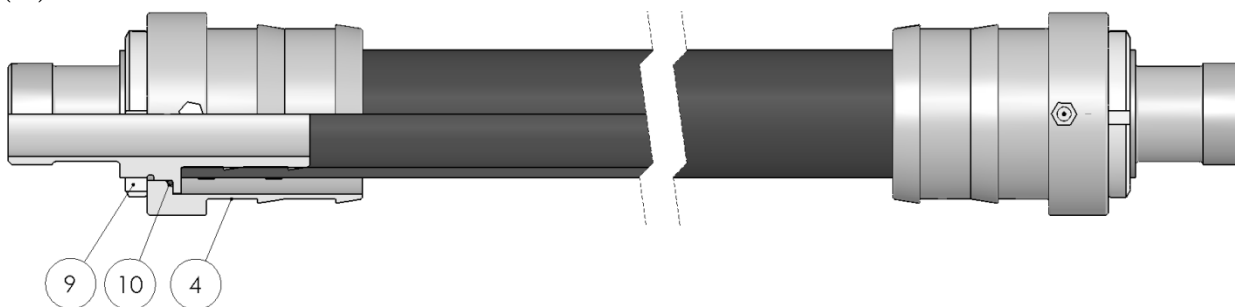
Die Sicherungsmuttern (9), die Flansche für den Pulsationsschlauch (Bauteil 4) und die O-Ringe (10) entfernen.
